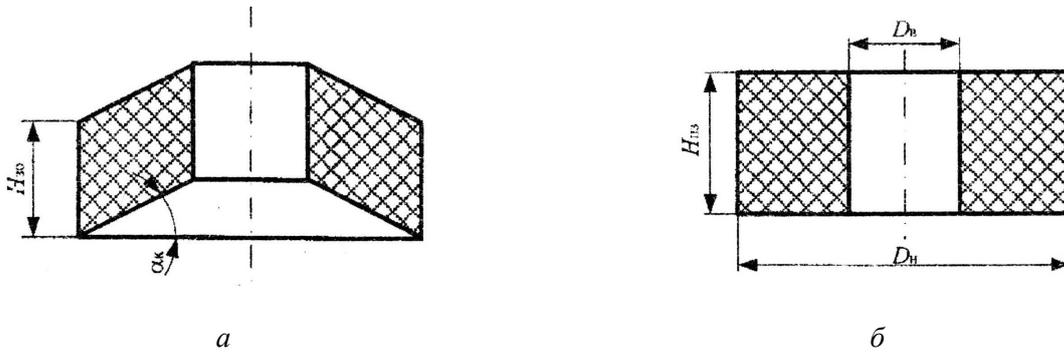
Формование заготовки конического УДЭ: заготовка (а) и предзаготовка (б)
